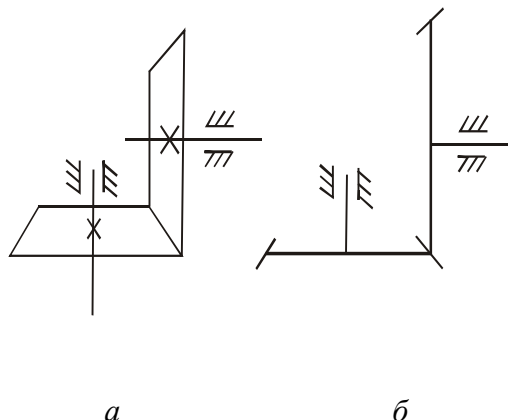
Коническая передача: а – колеса в зацеплении; б – колеса на кинематической схеме.
